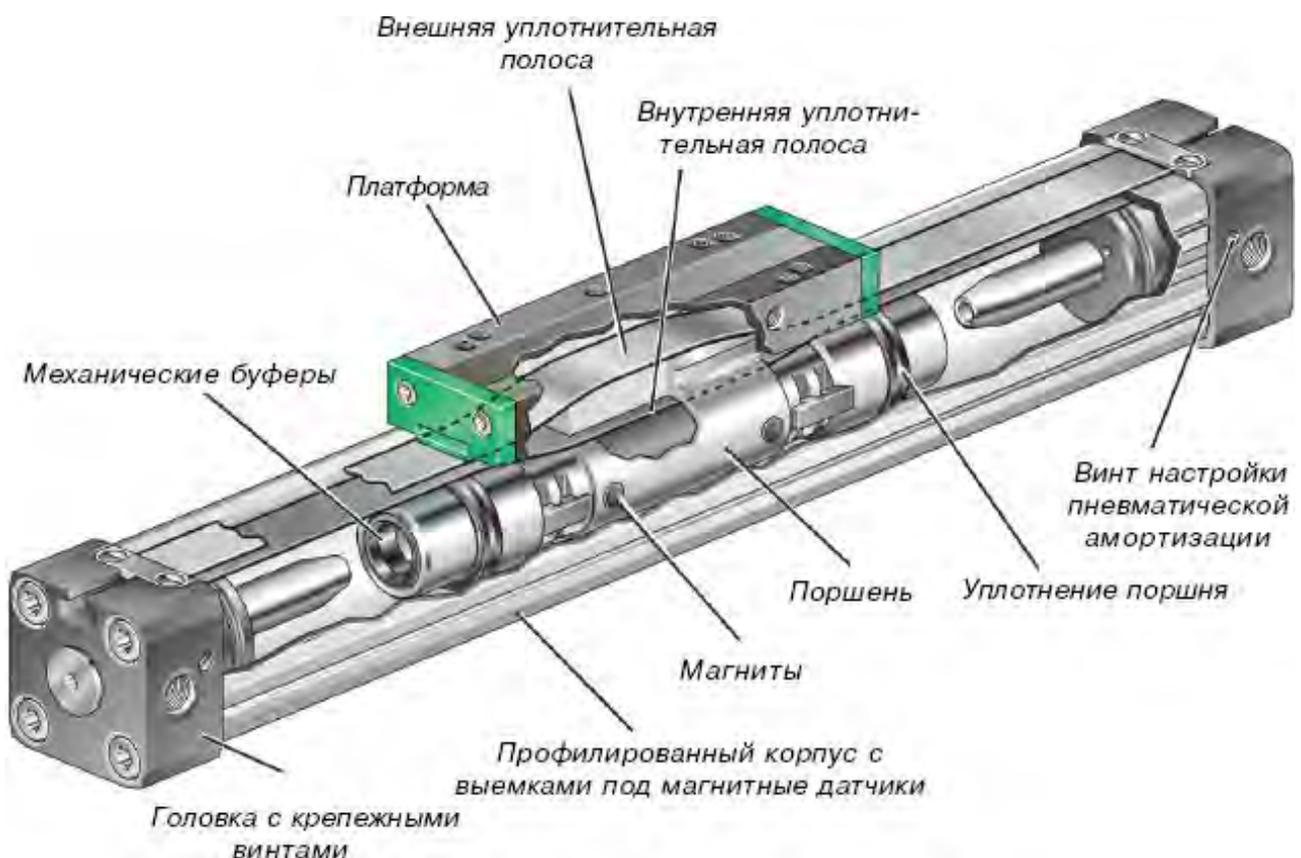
Пневматический бесштоковый цилиндр
